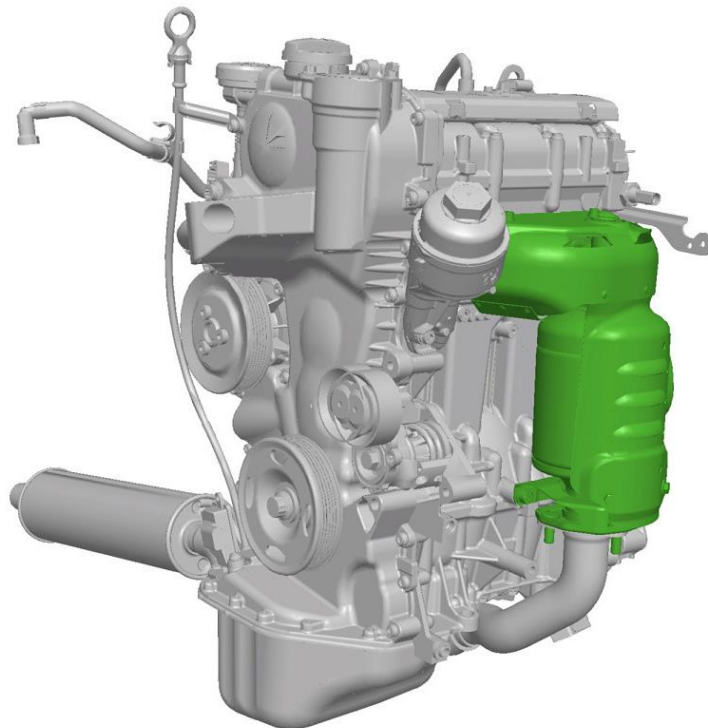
Parametry motoru 1,2 HTP [2]
